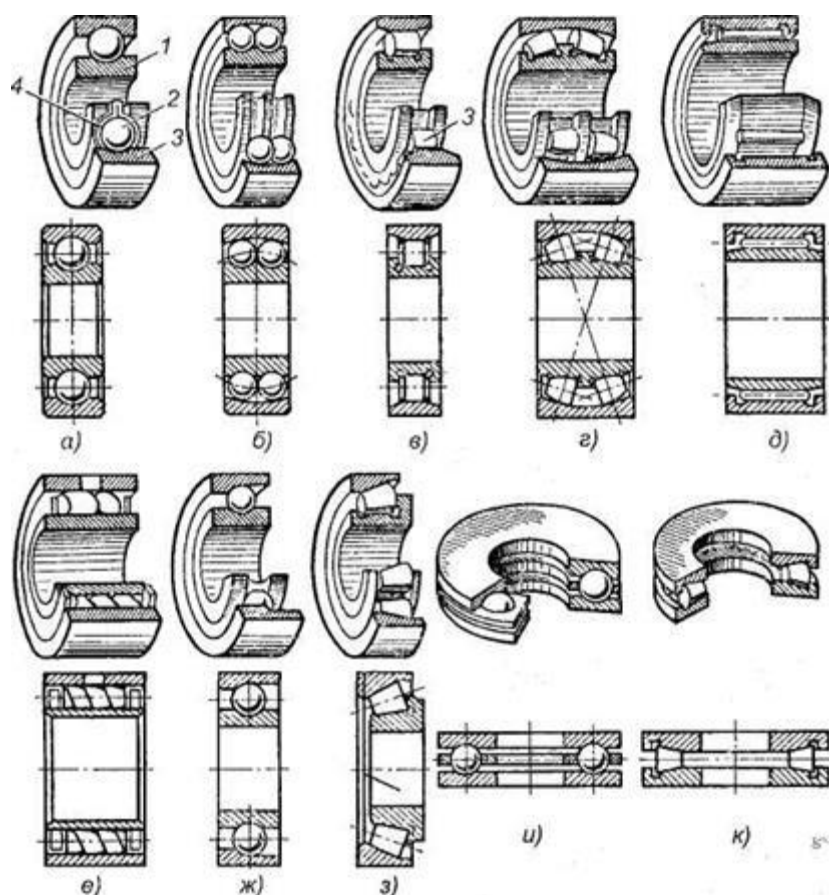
Подшипники качения: а, б, в, г, д, е — радиальные подшипники; ж, з — радиально-упорные подшипники; и, к — упорные подшипники; 1 — внутреннее кольцо; 2 — тело качения; 3 — наружное кольцо; 4 — сепаратор
